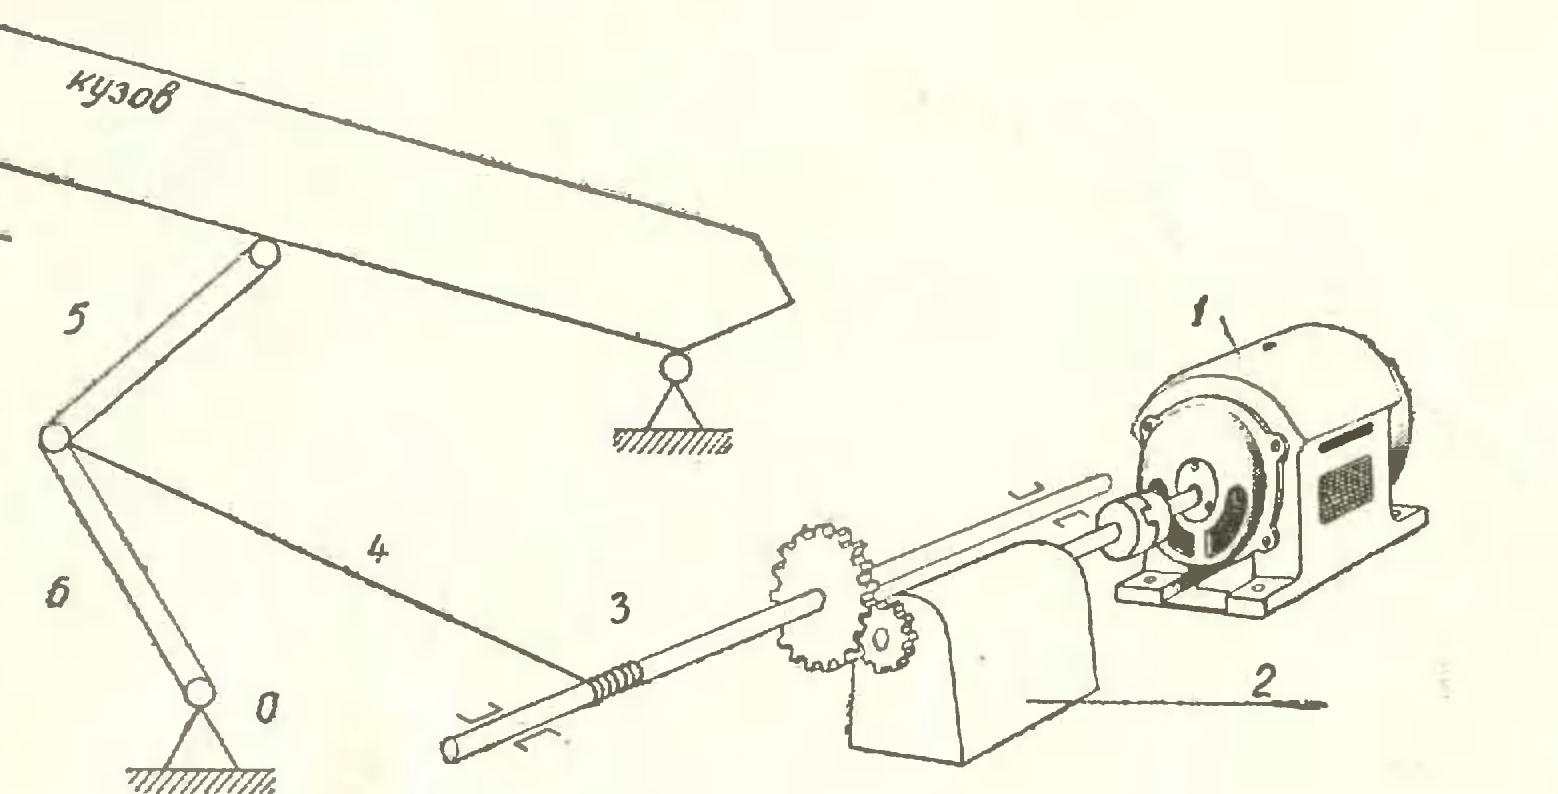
Механизм подъёма кузова: 1 — электродвигатель; 2 — редуктор; 3 — лебёдка; 4 — трос; 5 и 6 — рычаги; 0 — ось.
